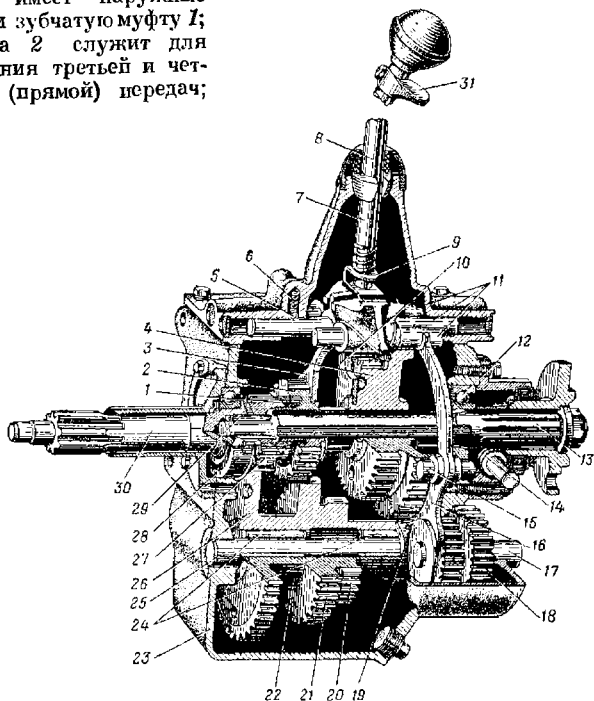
Четырехступенчатая коробка передач автомобиля ГАЗ-51.
